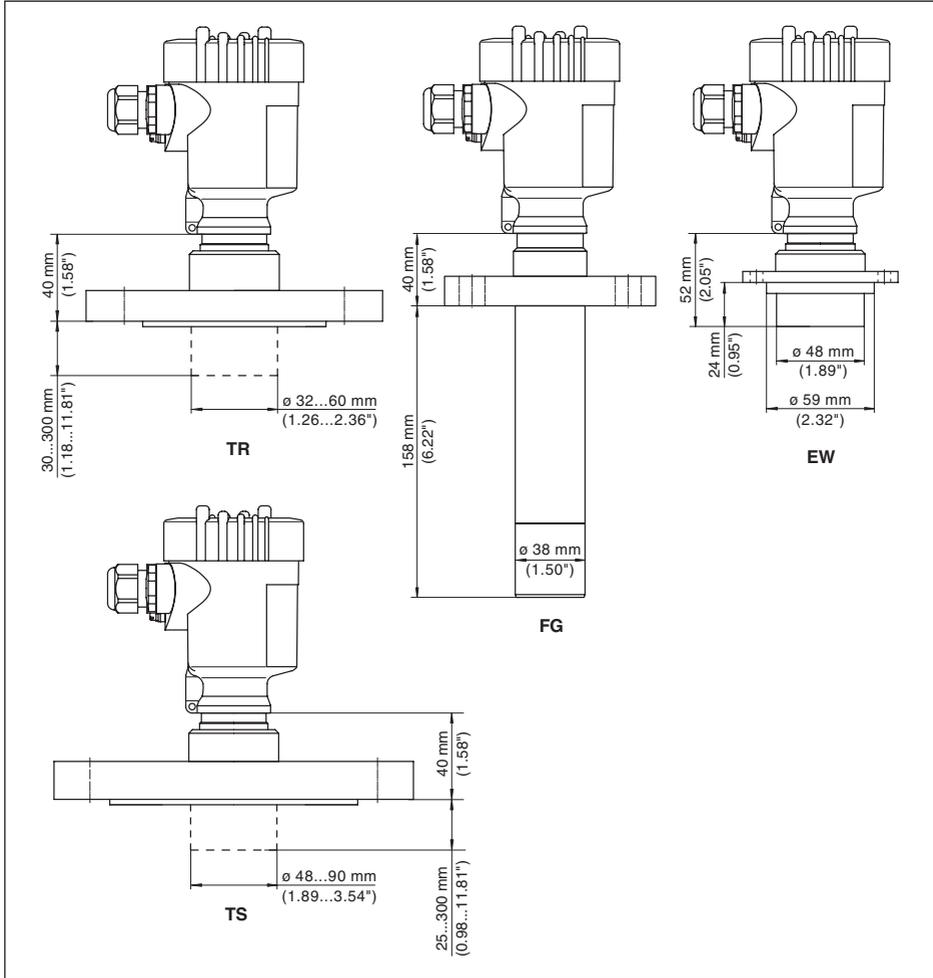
VEGABAR 52, conexão de flange para a indústria de papel: TR = flange DN 50 com tubo selecionável, TS = flange DN 80 com tubo selecionável, FG = flange com tubo para guarnição de torneira esférica, EW = flange para manômetro
